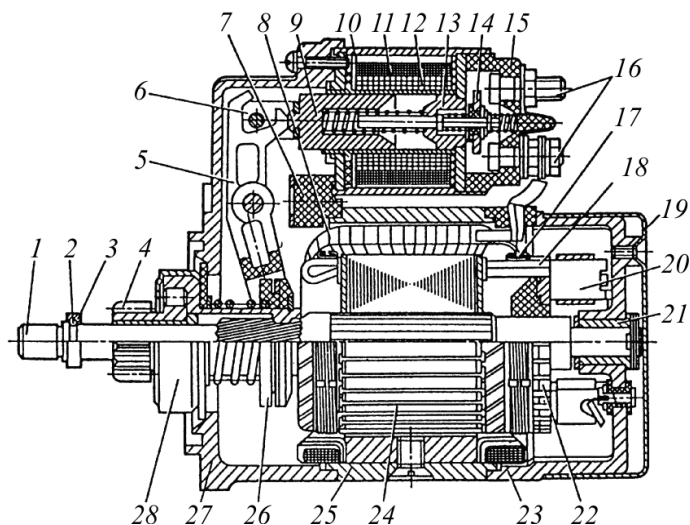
Стартер с одной опорой в крышке: 1 – вал якоря; 2 – замковое кольцо; 3 – упорное кольцо; 4 – шестерня привода; 5 – рычаг привода; 6 – тяга реле; 7 – уплотнительная заглушка; 8 – катушка обмотки возбуждения; 9 – якорь тягового реле; 10 – корпус тягового реле; 11, 12 – удерживающая и втягивающая обмотки; 13 – магнитопровод тягового реле; 14 – подвижный контакт; 15 – крышка тягового реле; 16 – контакты; 17 – бандаж лобовой части обмотки якоря; 18 – обмотка якоря; 19 – защитный кожух; 20 – щетка; 21 – вкладыш подшипника; 22 – торцевой коллектор; 23, 27 – крышки соответственно со стороны коллектора и привода; 24 – якорь электродвигателя; 25 – корпус; 26 – поводковая муфта; 28 – роликовая муфта свободного хода
